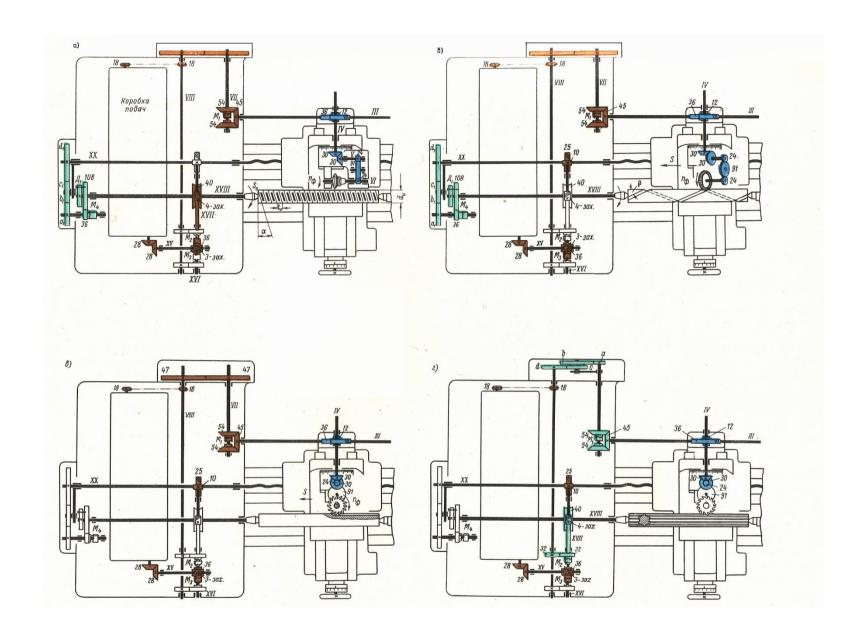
Схемы настройки резьбофрезерного станка модели 561
